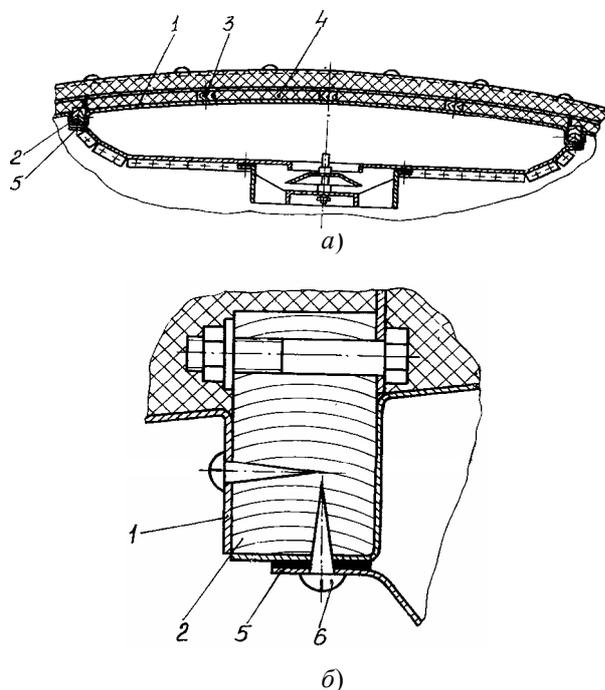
Поперечный разрез на вагоне модели 61-779: а – приточного воздуховода; б – узла крепления
